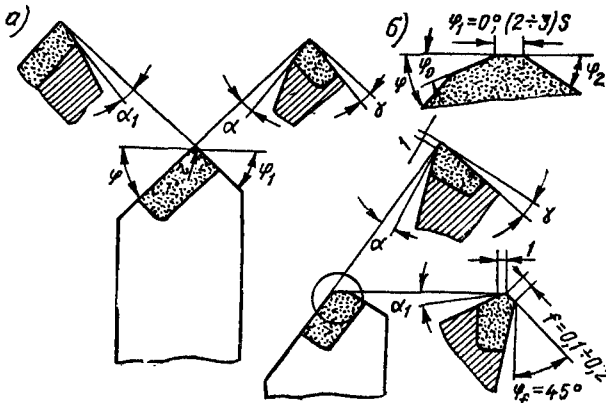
Твердосплавные резцы для тонкого и чистового точения.
